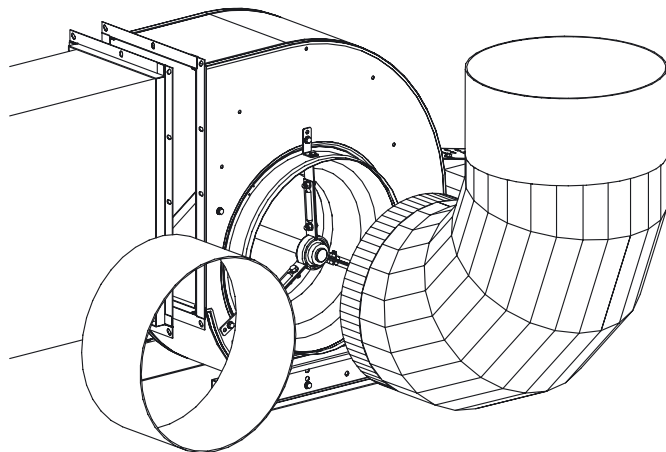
Espace nécessaire au remplacement des roulements.
